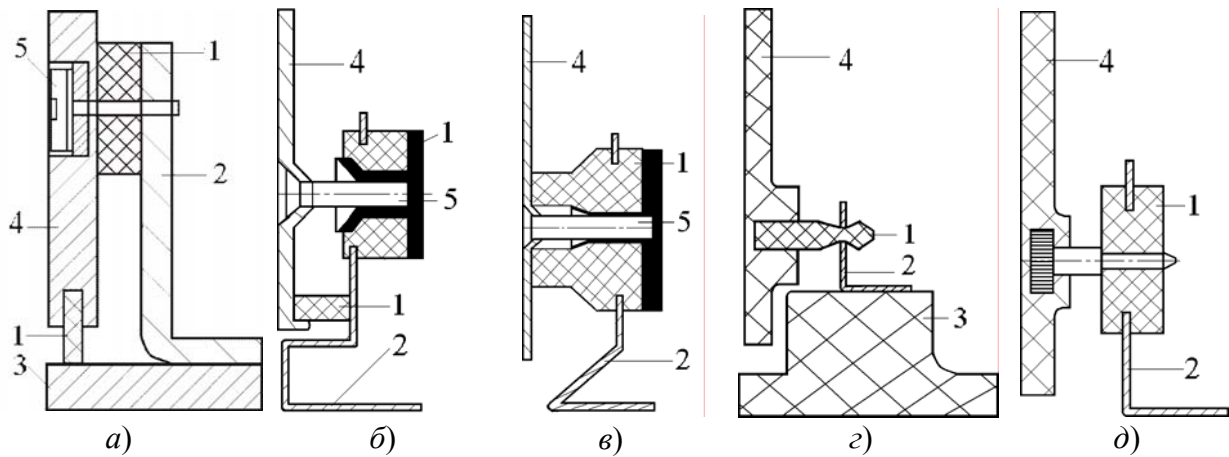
Примеры звукоизоляторов в местах крепления боковой стенки корпуса к основанию:
